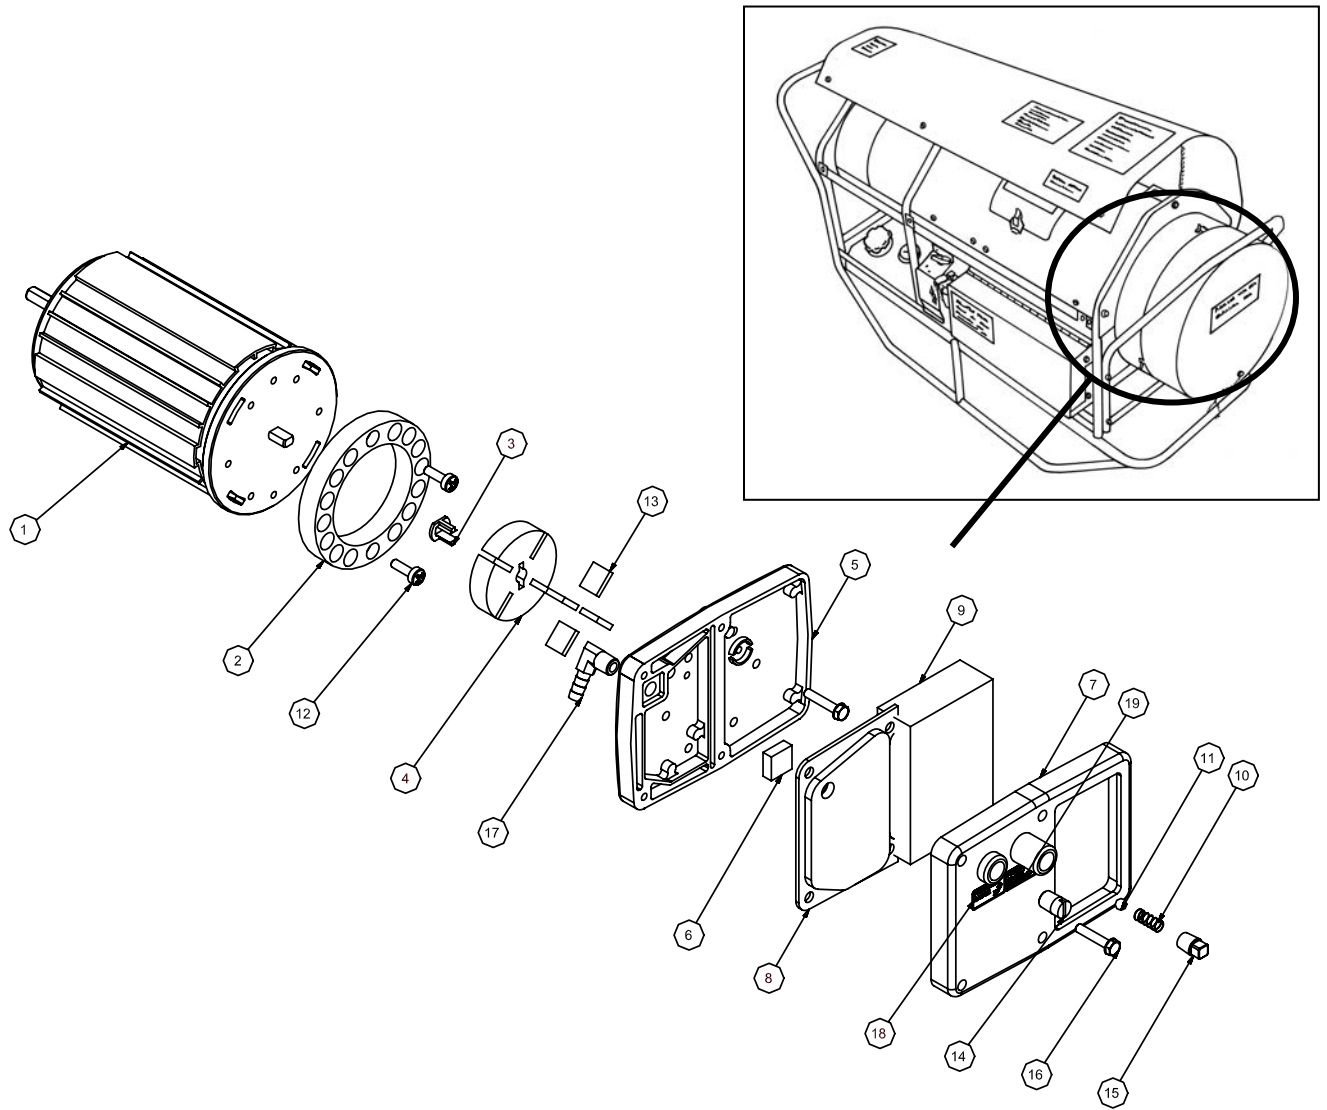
Assemblage De Moteur Et Pompe 53485
